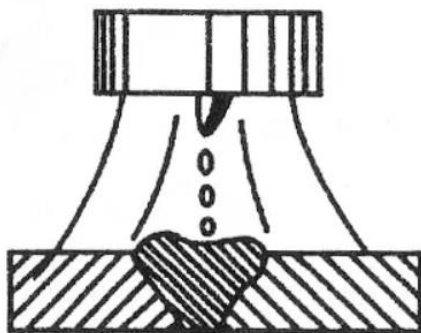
Струйный перенос металла в сварочную ванну
